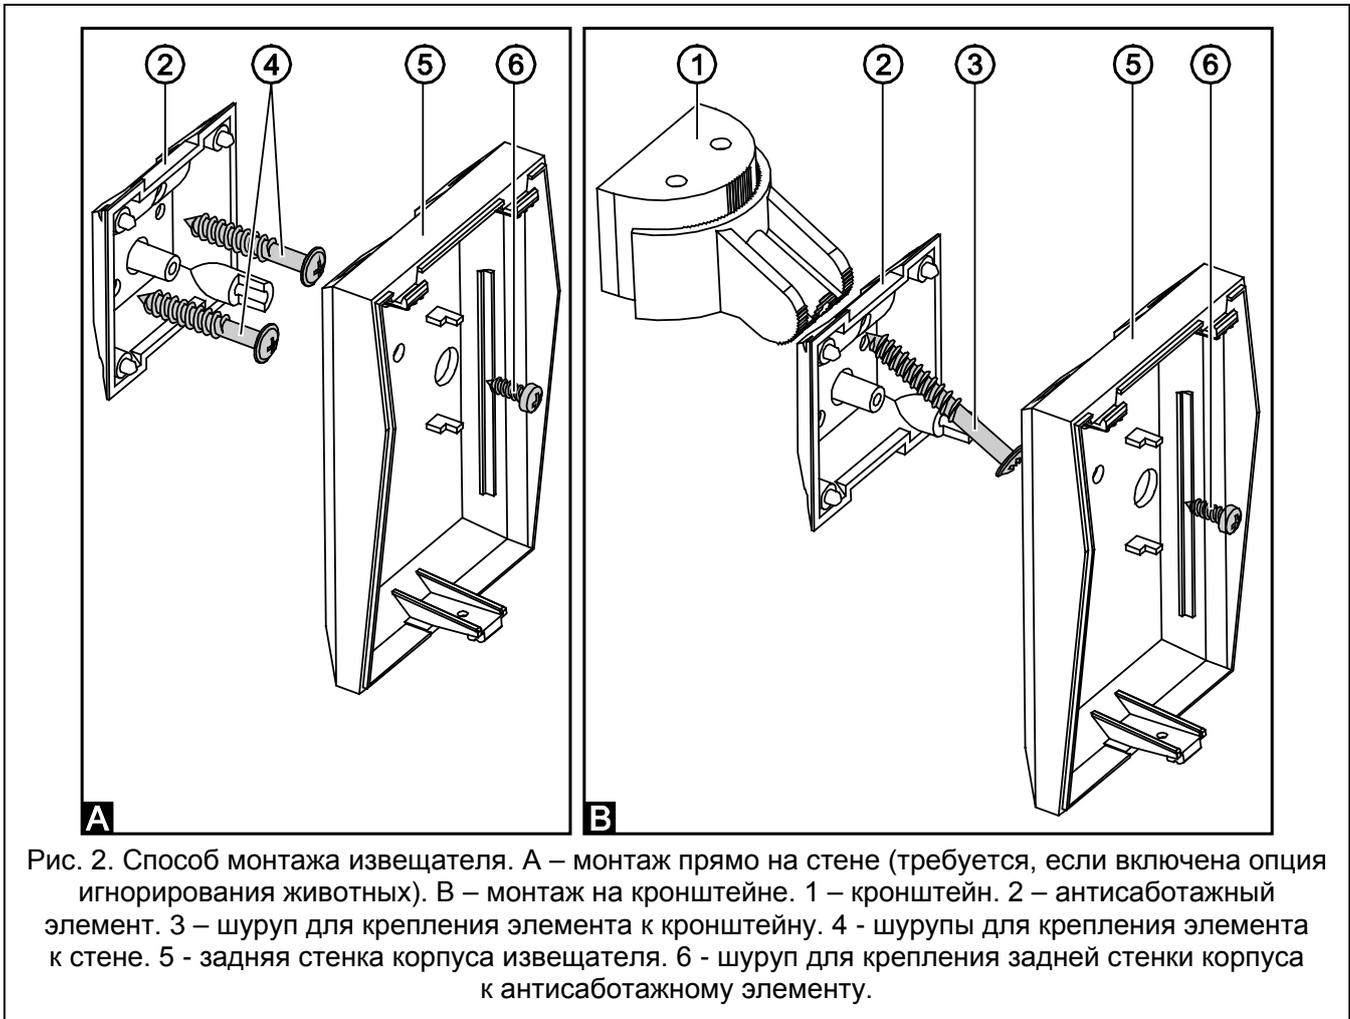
Способ монтажа извещателя. А – монтаж прямо на стене (требуется, если включена опция игнорирования животных). В – монтаж на кронштейне. 1 – кронштейн. 2 – антисаботажный элемент. 3 – шуруп для крепления элемента к кронштейну. 4 – шурупы для крепления элемента к стене. 5 – задняя стенка корпуса извещателя. 6 – шуруп для крепления задней стенки корпуса к антисаботажному элементу.
